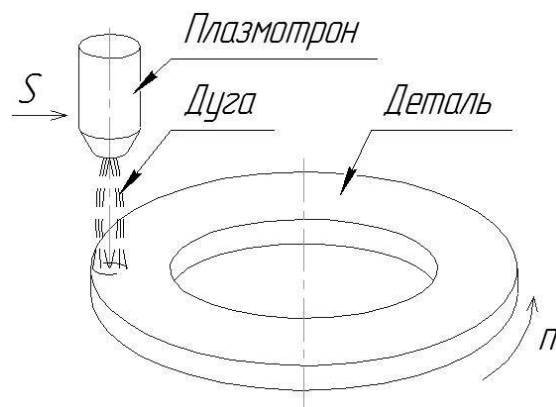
Схема плазменной наплавки торцевых поверхностей
